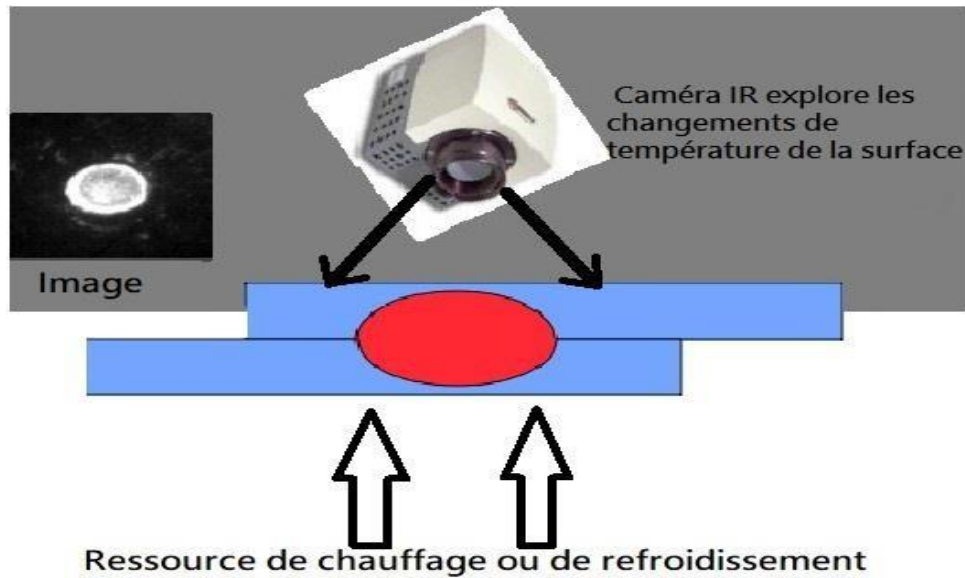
Principe de l'inspection de la qualité des soudures par caméra IR [34].
